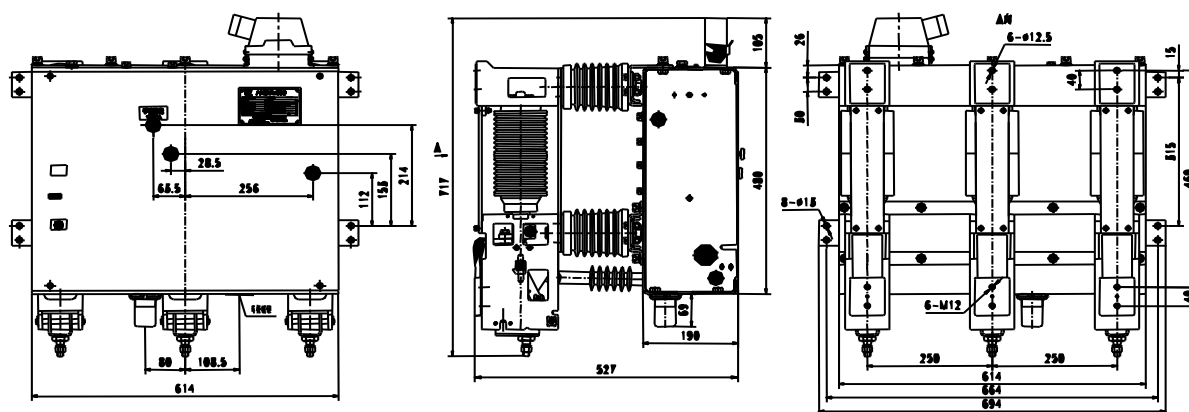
ZN65-12 型户内高压真空断路器的结构外形和尺寸
